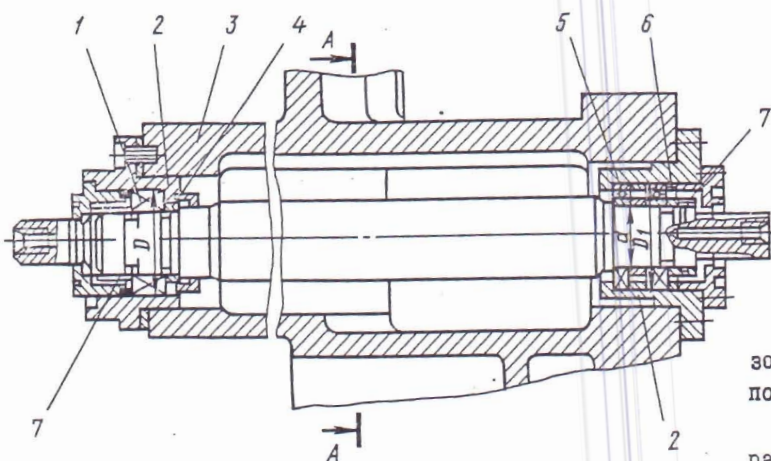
Шпиндель шлифовальной головки станка ЗЕ710А
